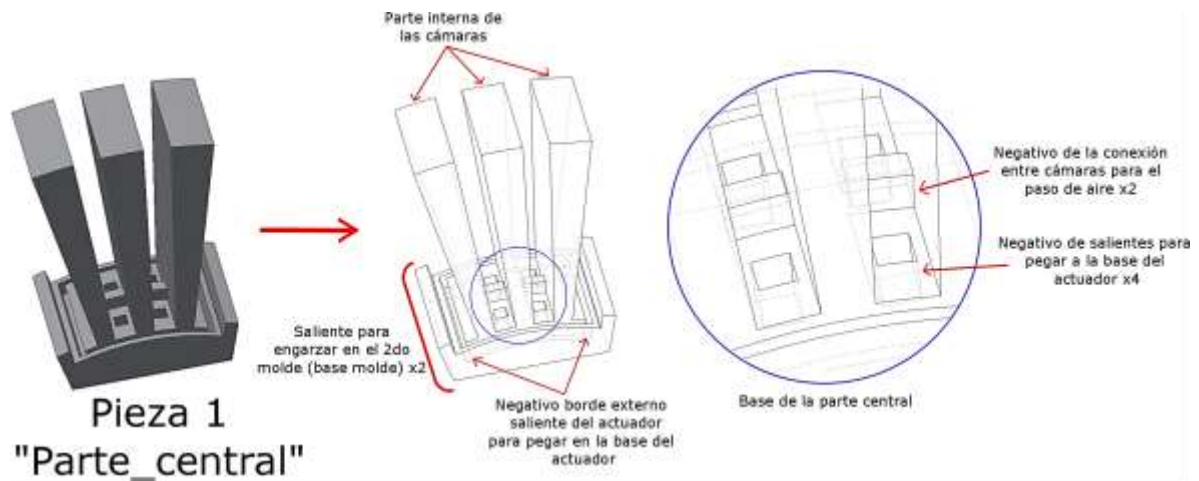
Detalle de la pieza 1 del molde para el cuerpo del actuador blando
